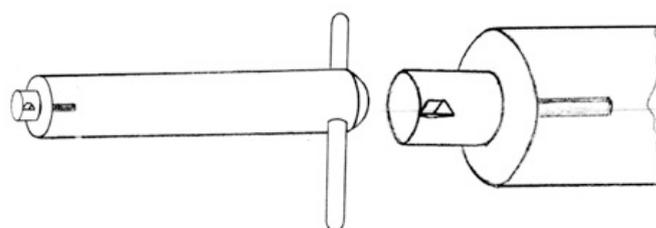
Общий вид и рабочая часть инструмента для выполнения «заякоряемых» отверстий.
